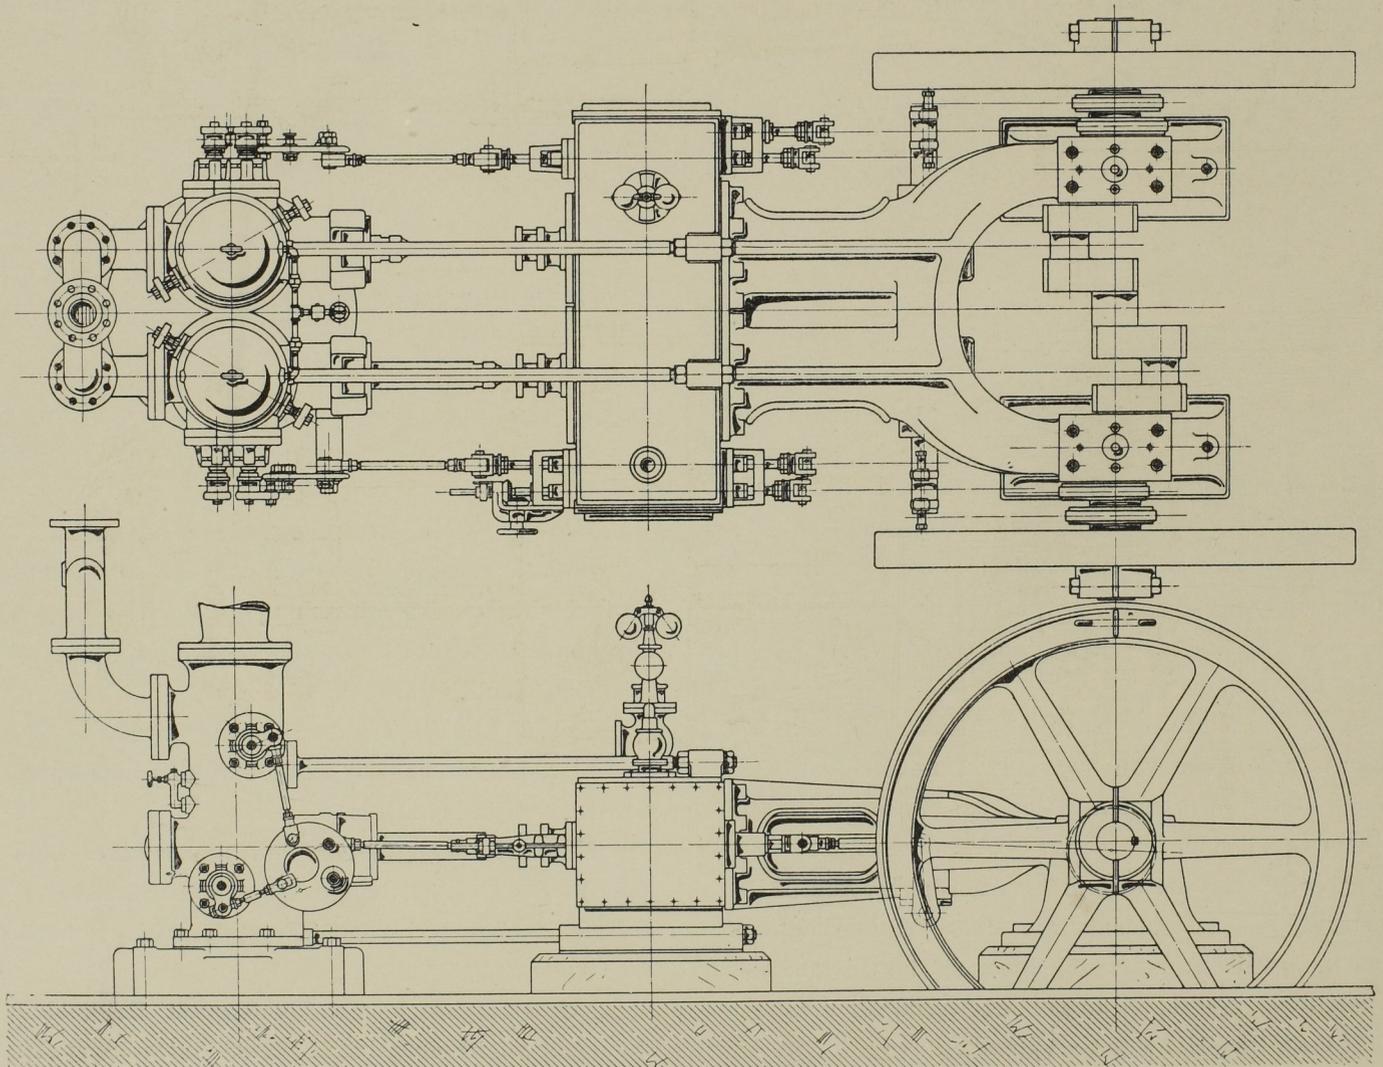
Seitenansicht und Grundriss der Maschine. Massst. 1:36.
